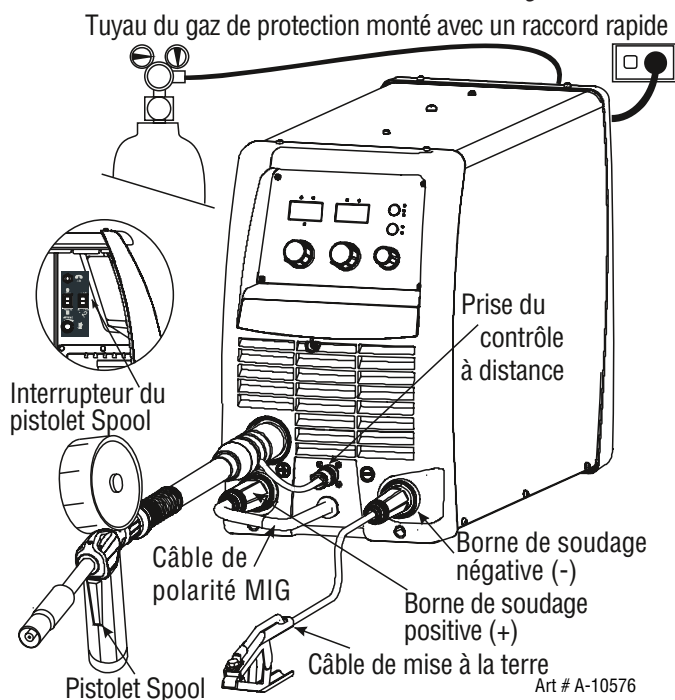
Configuration pour le soudage au moyen du pistolet Spool avec le fil MIG protégé par gaz
